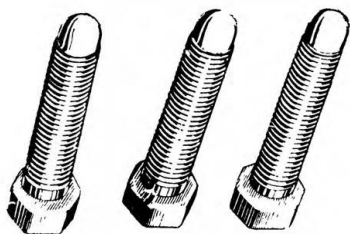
Три болта 47001-1-054П для выпрессовки венца барабана дет. 237-24-9 планетарного механизма поворота
